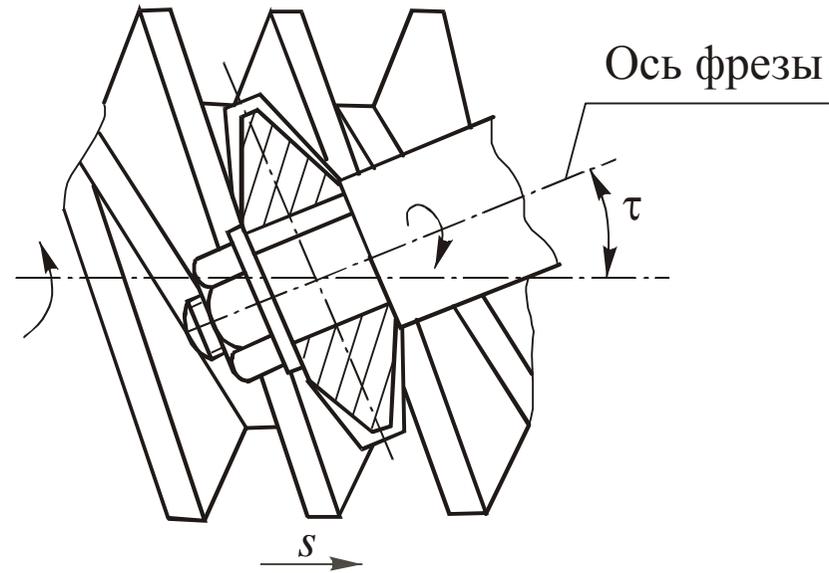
Схема установки дисковой фрезы относительно заготовки
